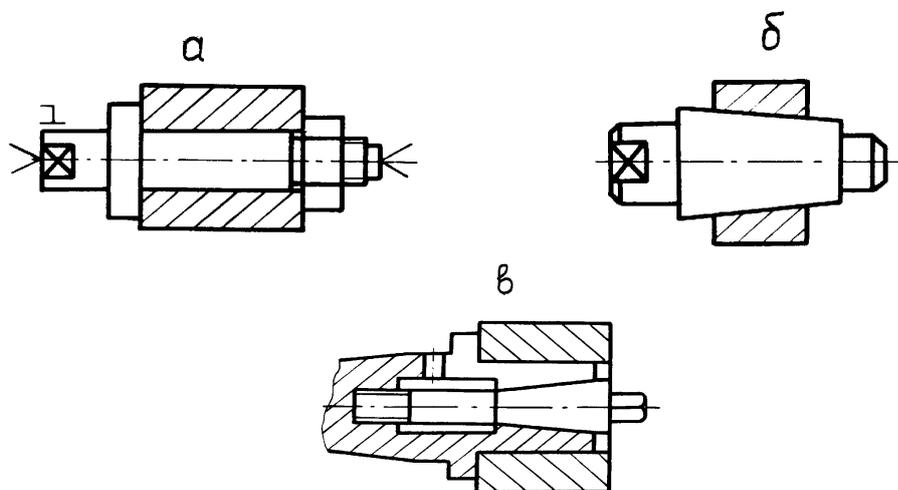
Оправки: а — цилиндрическая; б — коническая; в — цанговая
